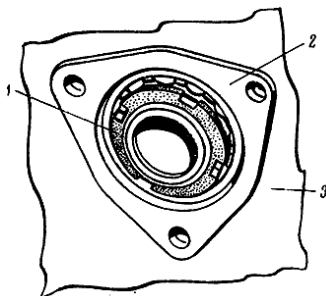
Отворачивание гайки крепления внутреннего вала: 1-гайка; 2- гнездо подшипника; 3- корпус КПП
